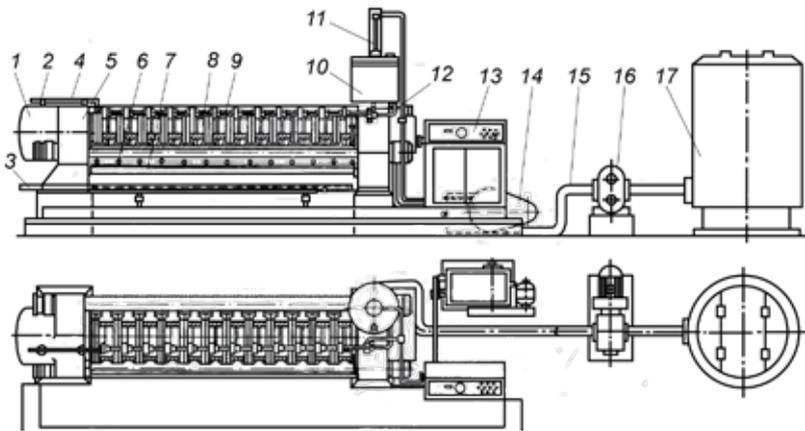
Гидропрессовая установка с горизонтальным 12-чашечным прессом
